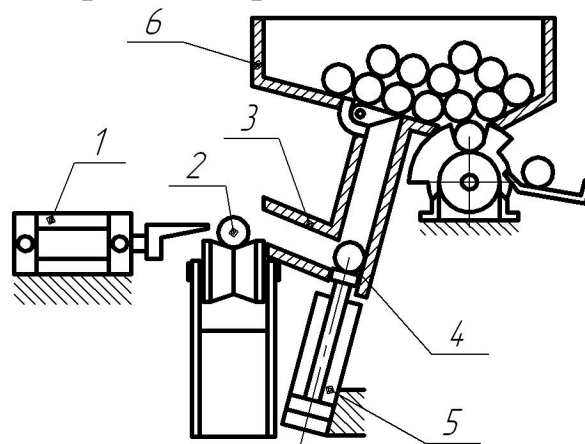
Schéma principale du manipulateur: vérin 1; 2 - billette; 3 - glissière de guidage; 4 - billette; 5 - vérin 5; 6 - accumulateur.
